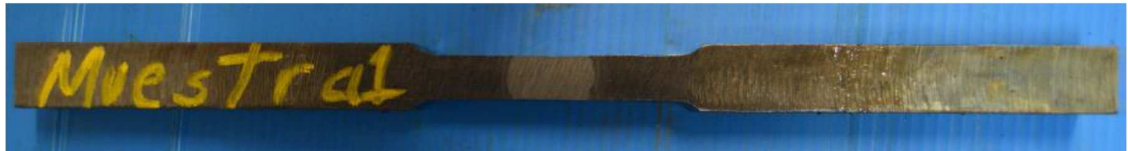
10 Fotografía de la probeta maquinada de la soldadura con cara de raíz de 5 mm
